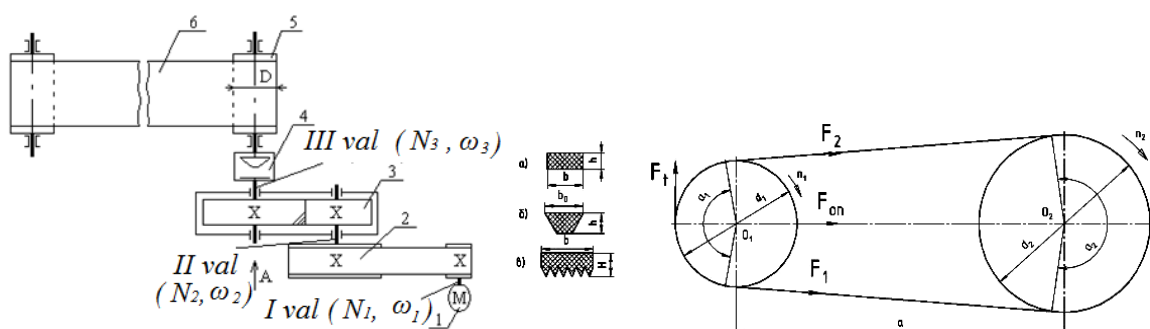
Привод ленточного конвейера с цилиндрическим редуктором и ременной передачей.
